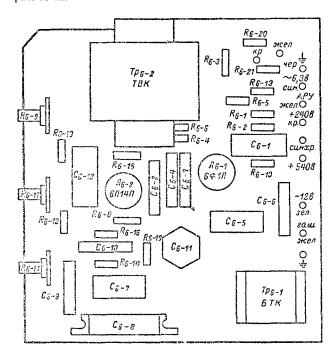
Расположение деталей на плате кадровой развертки телевизора «Нева».
